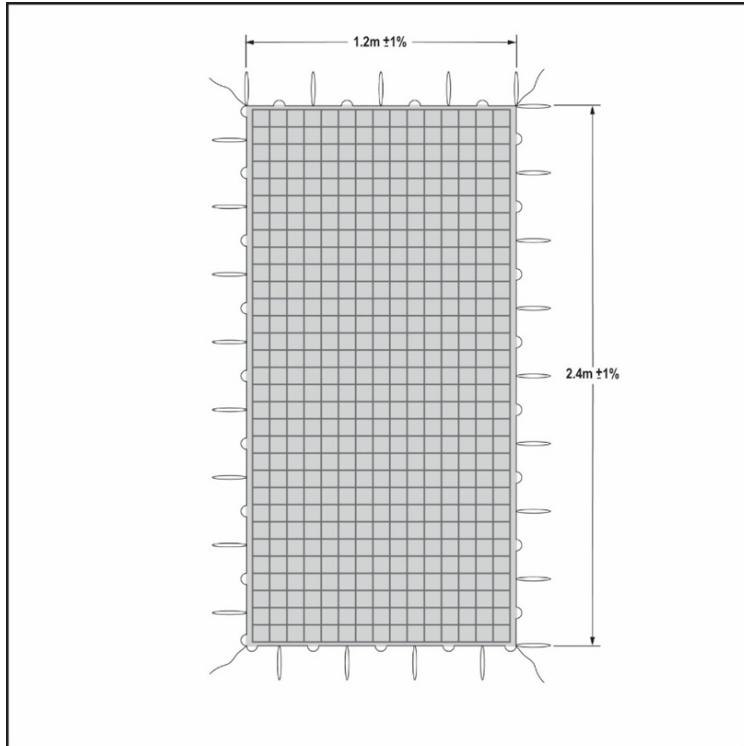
Schéma d'un EITE de 2,4 m sur 1,2 m
